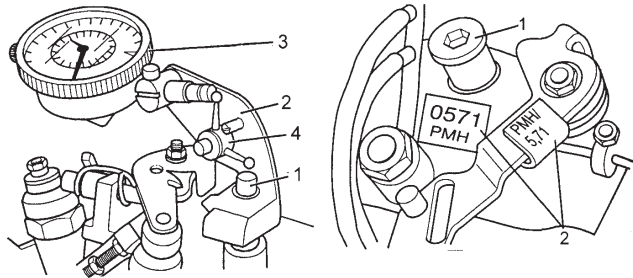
Установка индикаторного приспособления на крышке ТНВД Lucas DPC:
